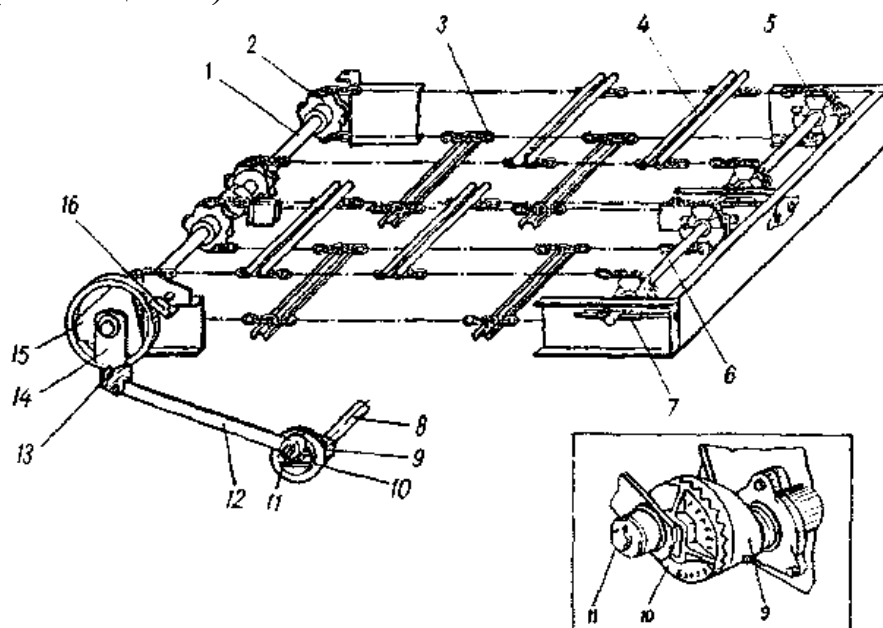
Транспортер: 1 – вал ведущий; 2 – звездочка; 3 – цепь; 4 – скребок; 5 – ролик; 6 – вал ведомый; 7 – устройство натяжное; 8 – вал второй ступени редуктора; 9 – корпус кривошипа; 10 – диск кривошипа; 11 – палец; 12 – шатун; 13 – собачка рабочая; 14 – щека; 15 – колесо храповое; 16 – собачка обратного хода
